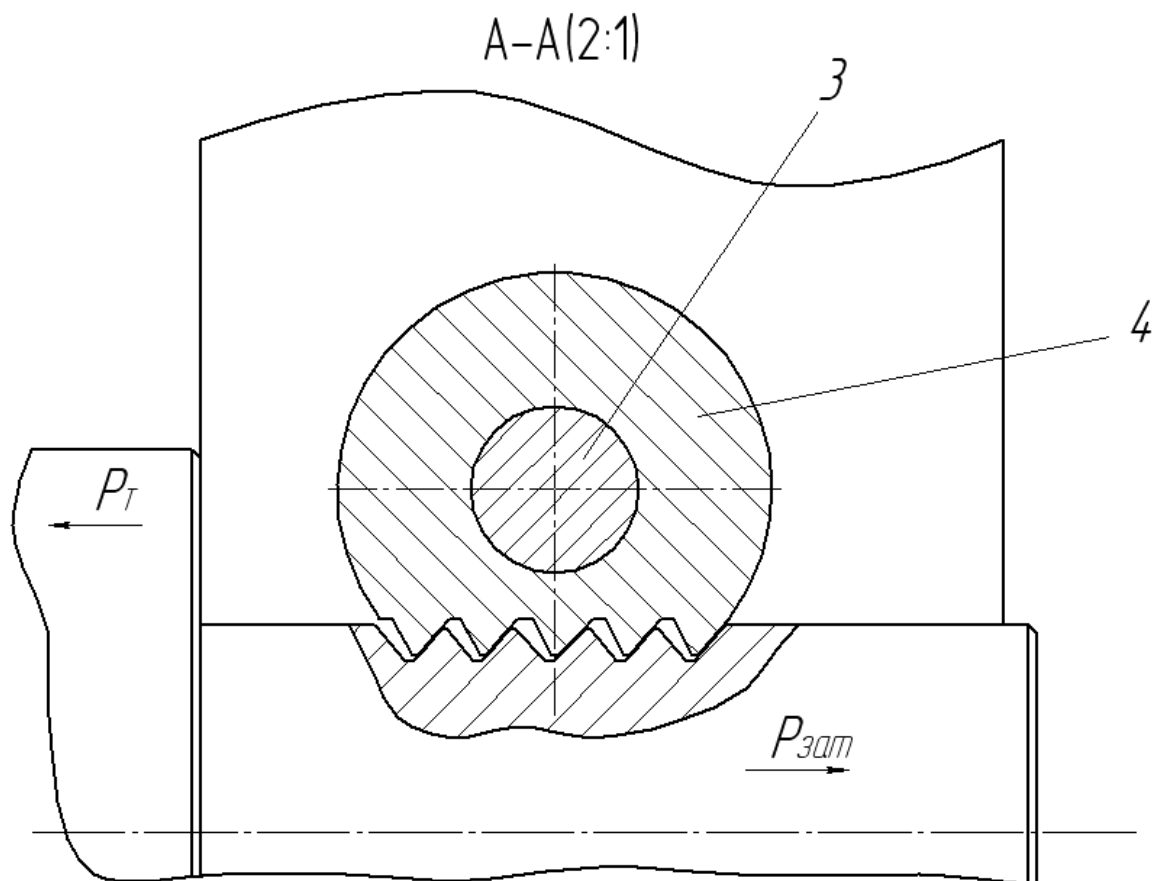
Розроблена конструкція зубчастого сухаря для затиску циліндричного хвостовика: 1. Циліндрична гайка; 2. Револьверна головка; 3. Гвинт; 4. Зубчастий сухар; 5. Орієнтаційний палець
